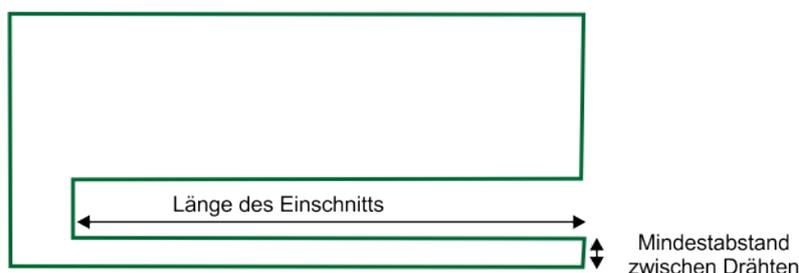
Standorte mit langen, isolierten Einschnitten
